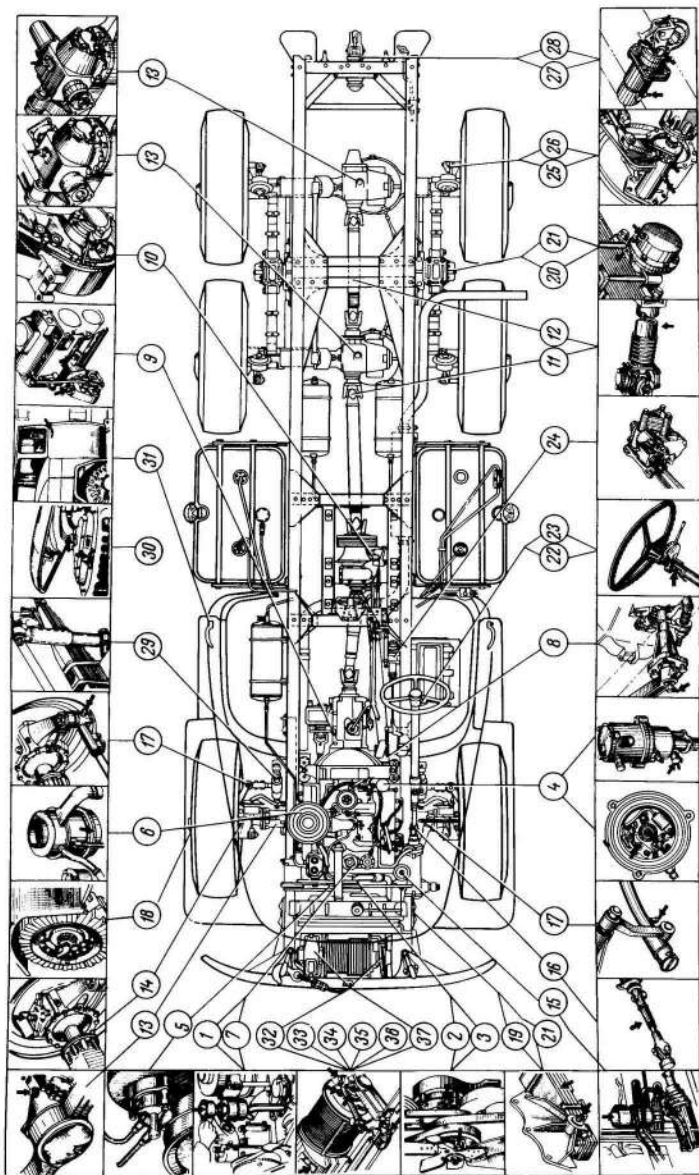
Схема сборки автомобиля ЗИЛ-131
